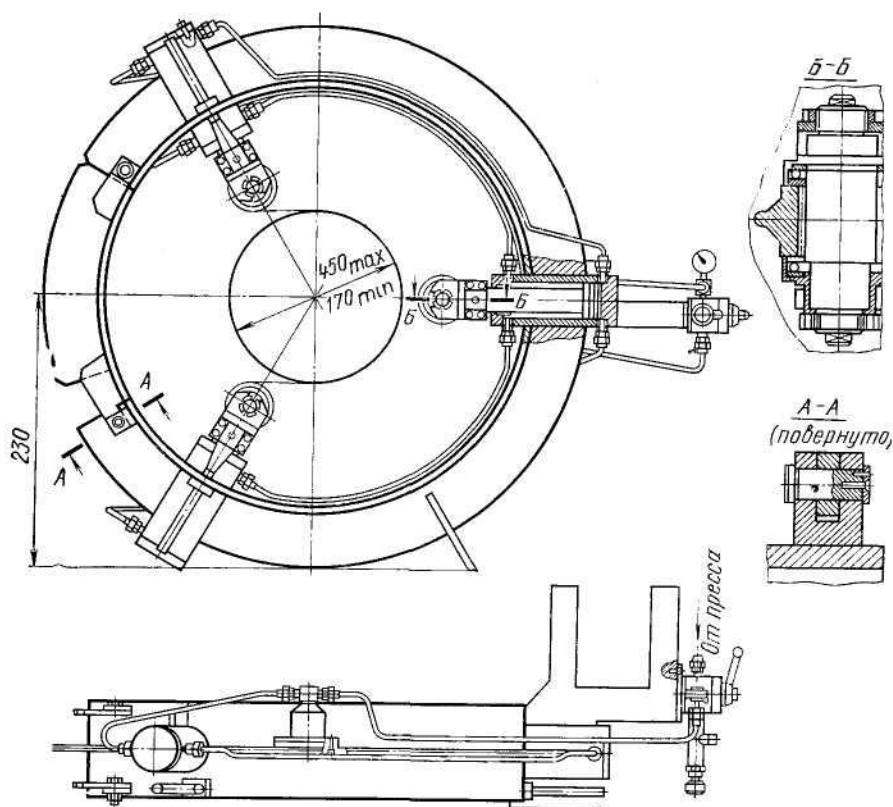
Трехроликовое приспособление для обработки деталей
